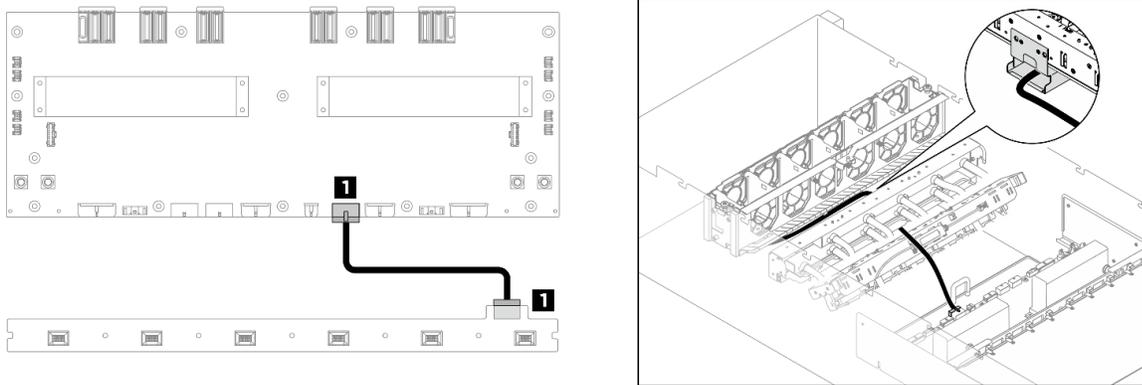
Roteamento de cabos da placa de controle do ventilador frontal
